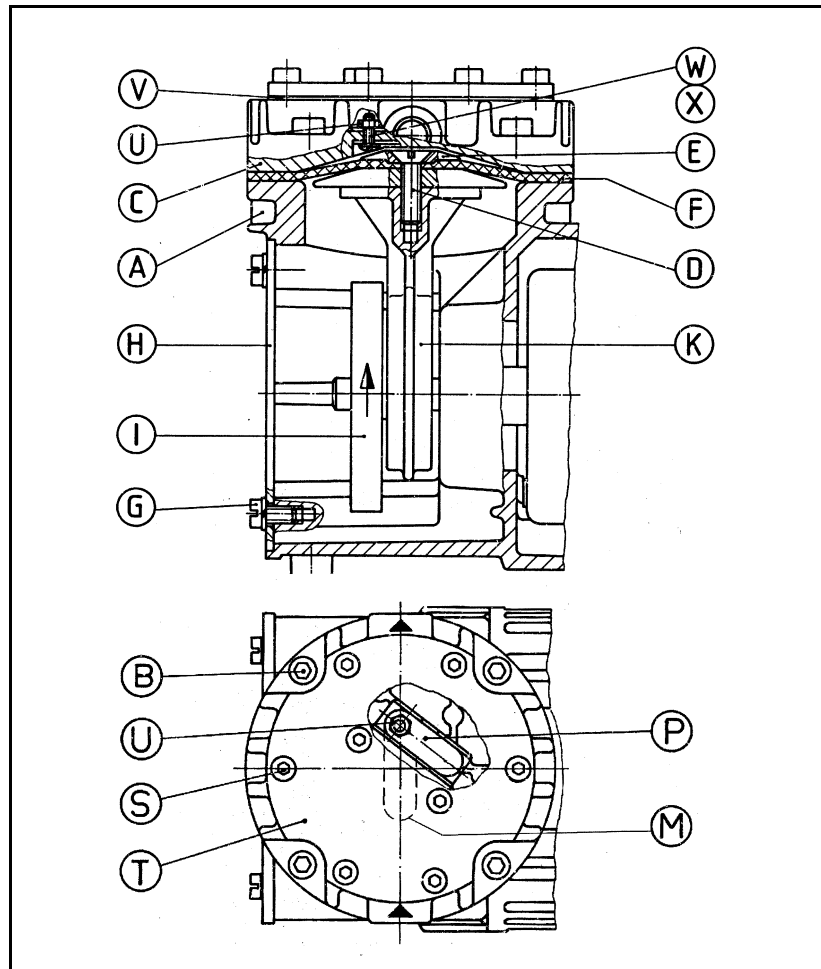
Pumpenteile für Ausführungen mit Aluminiumkopf
